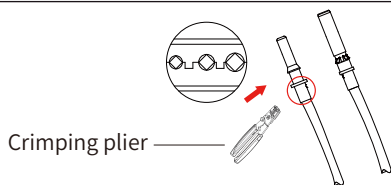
Crimpen des Kontaktstifts an den Draht
